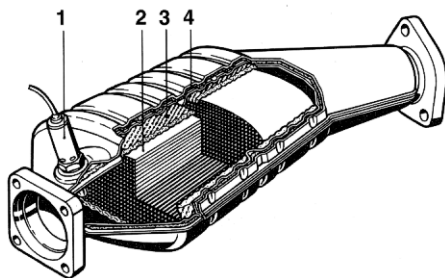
Трехкомпонентный каталитический нейтрализатор: 1 – λ -зонд; 2 – монолитный керамический блок из силиката алюминия; 3 – монтажный элемент в виде проволочной сетки; 4 – термостойкий корпус с двойными стенками.
